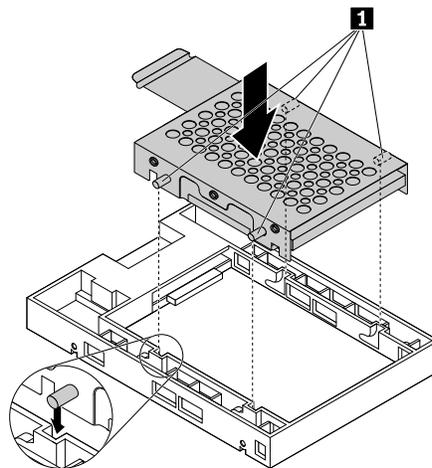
Вставка металлической скобы в пластиковую раму конвертера
